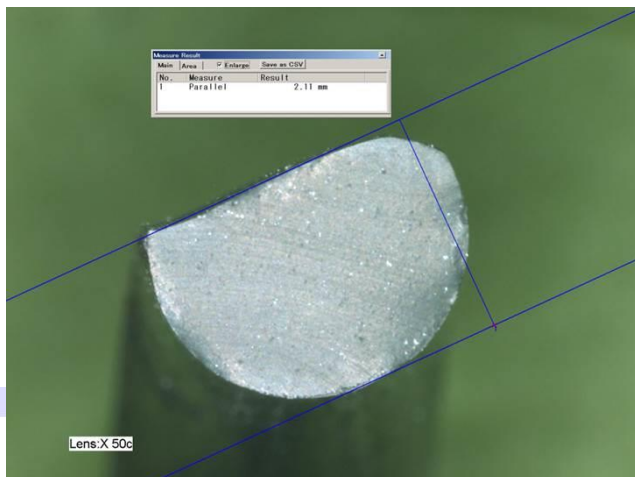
Abgeriebener O-Ring (EPDM, 70 ShA) aus „statischer“ Abdichtung mit zu großem druckbedingten Axialhub; Kolbeneinbauraum: Kolben mit Stahlklammer fixiert, gab unter Druck (10 bar) 0,5-1 mm nach, Durchmesserspiel ca. 0,5 mm, exzentrische Lage
